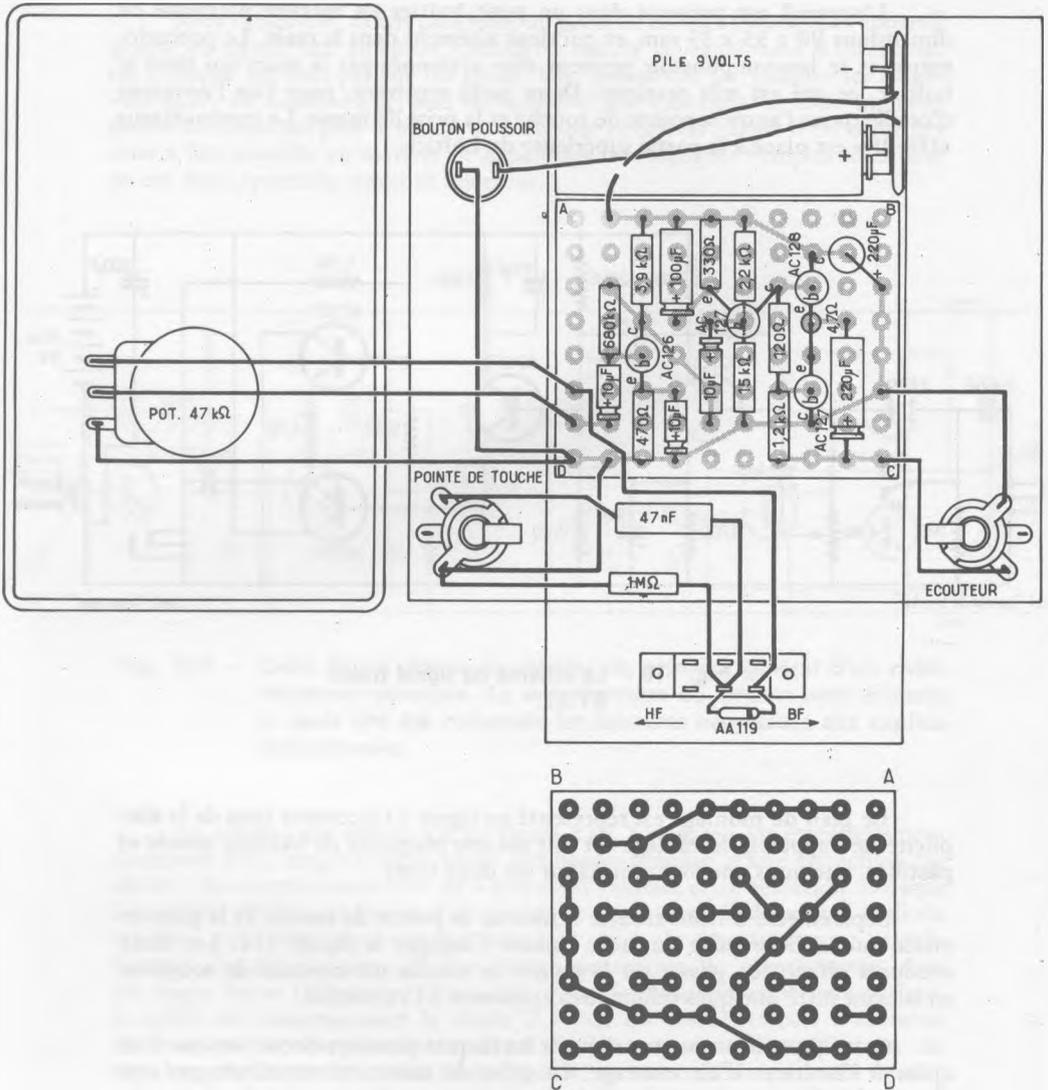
Le plan de câblage et la disposition dans le coffret.
